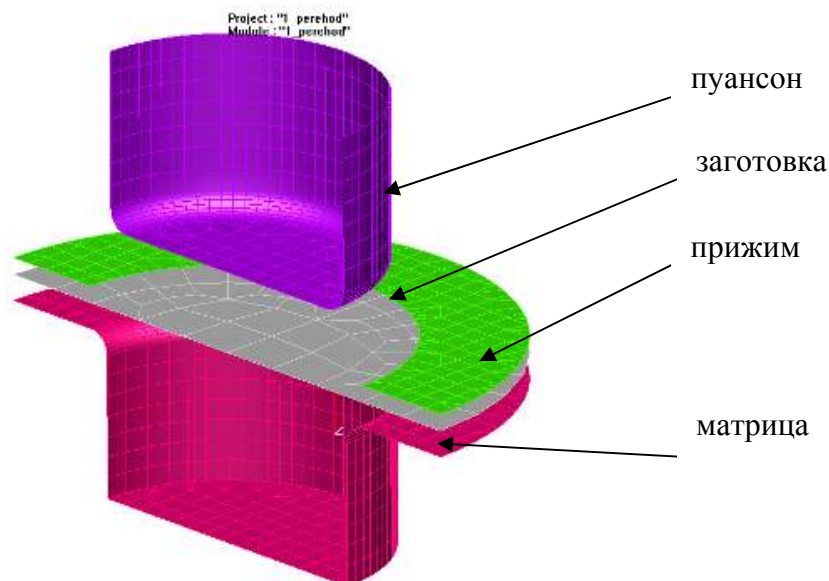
Конечно-элементные модели пуансона, прижима, матрицы и заготовки в программе PAM-STAMP
